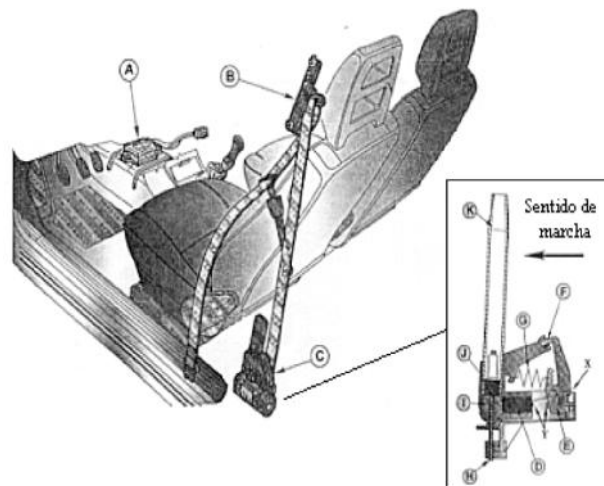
Pretensores por bobinador pirotécnico y mando mecánico
